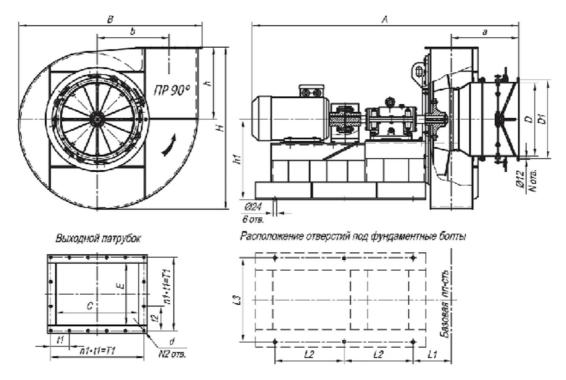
Габаритные и присоединительные размеры тягодутьевых машин типа ВДН и ДН №6,3-13 исп-3.
